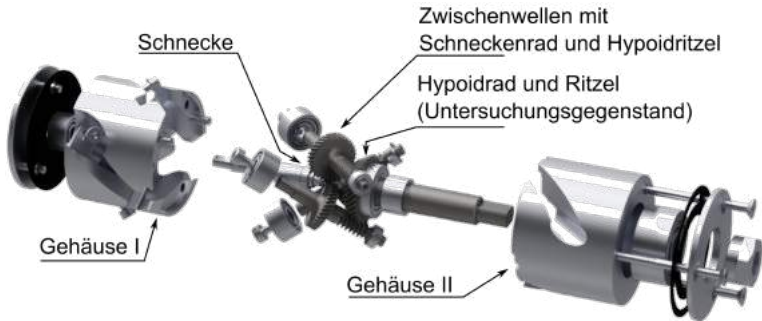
Explosionszeichnung des zweiten Prototyps.
